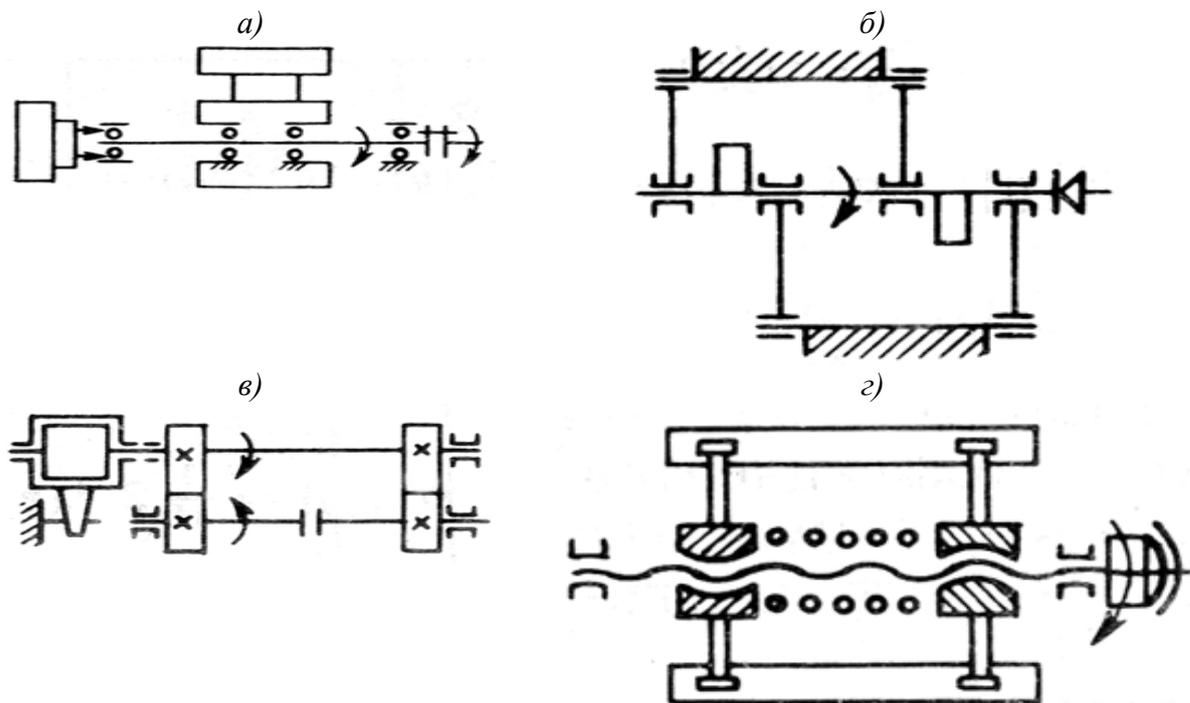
Схемы стендов для испытаний сборочных единиц (узлов):
